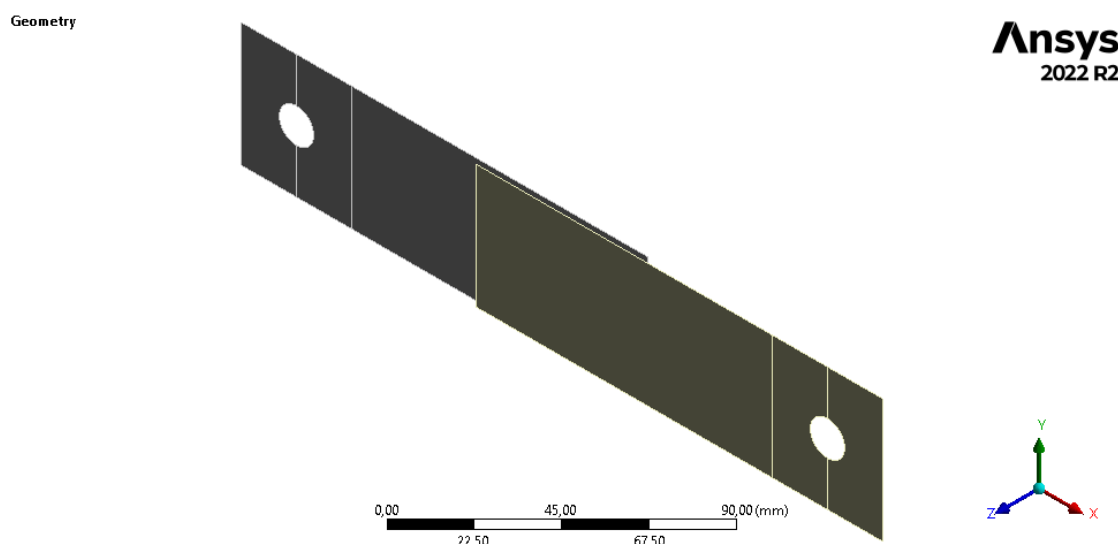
Vista isométrica de la geometría de las probetas de las chapas soldadas
